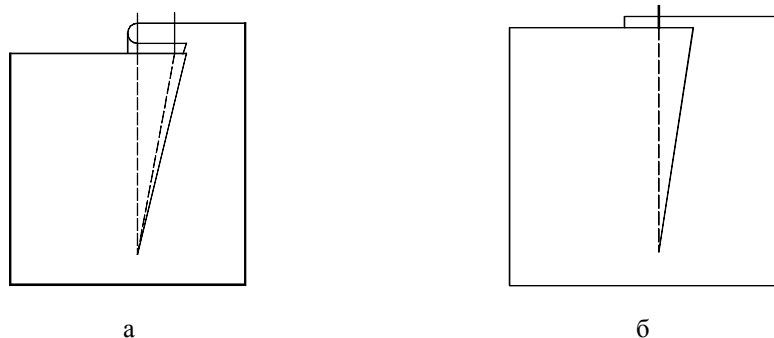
Монтажные схемы конструкций разрезных выточек, которые обработаны: а – накладным швом с закрытым срезом; б – накладным швом с открытыми срезами
